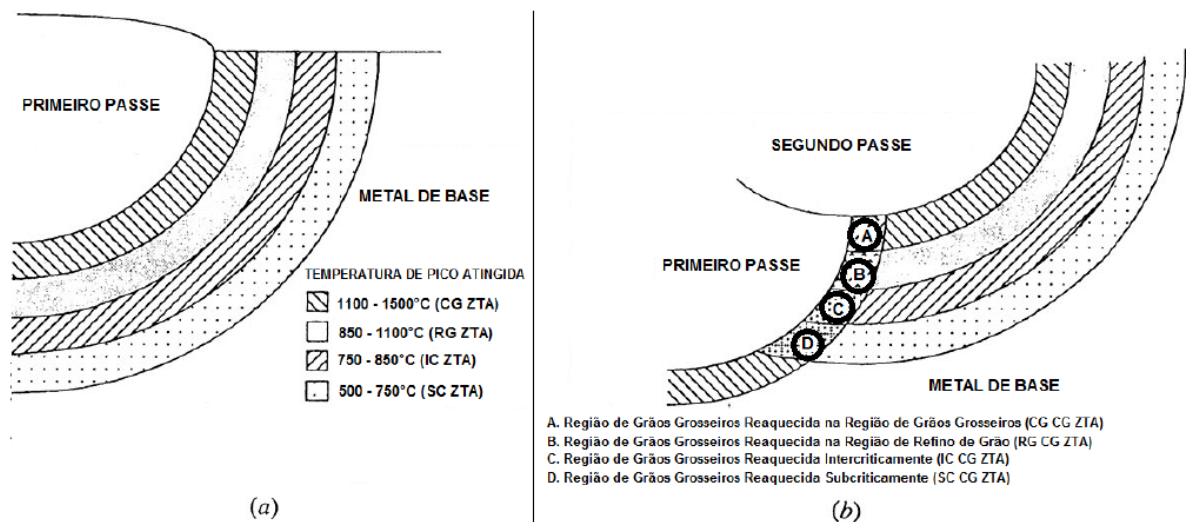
Representação esquemática da soldagem (a) de um único passe (b) multipasses.
